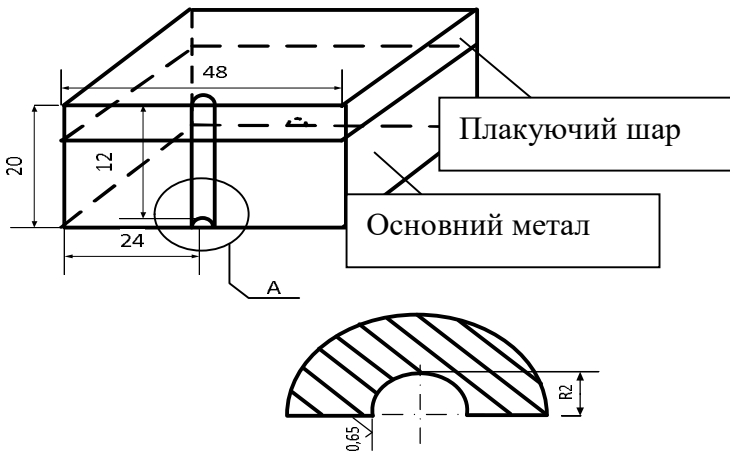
Зразки для випробувань шва біметалевих зварних з'єднань.
